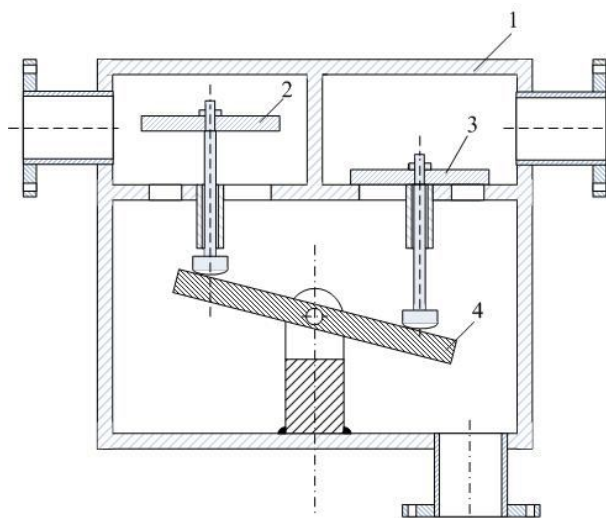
Внешний вид ПП с чашечным клапаном:
